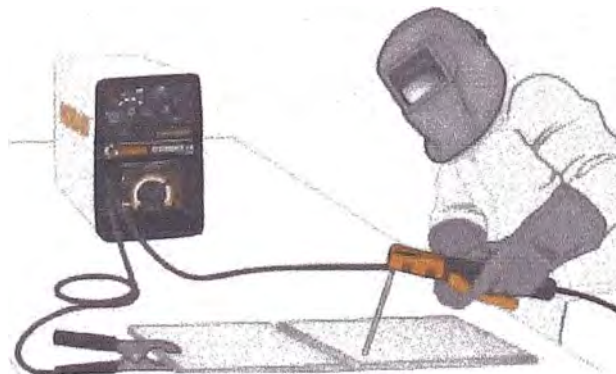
Disposición para soldadura de arco metálico recubierto (Fuente: Hobart Welders)
